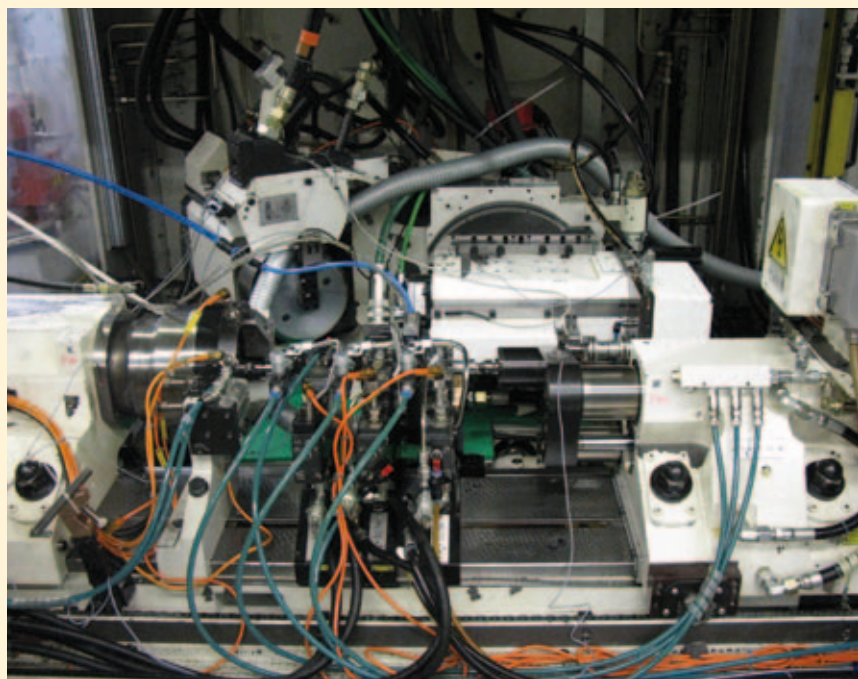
Versuchsaufbau: Schleifen mit Minimalmengenschmierung.
